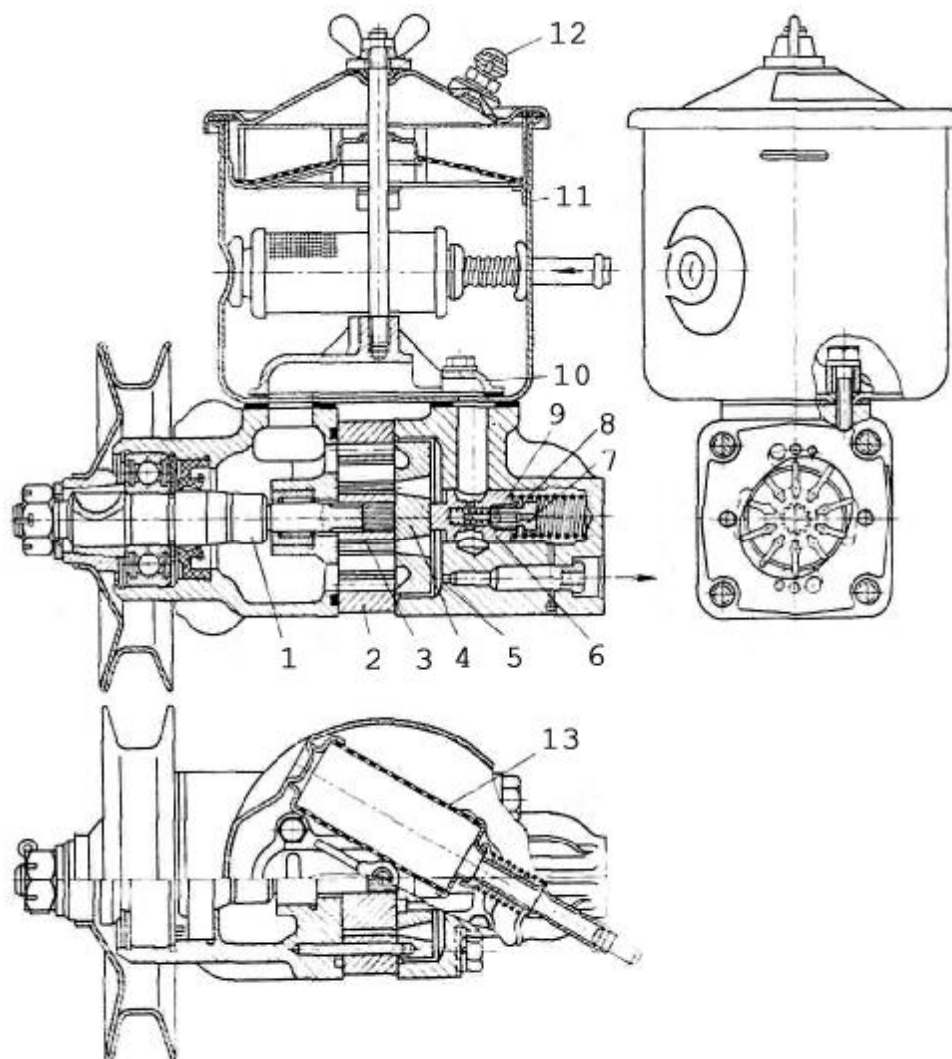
Пластинчатый гидронасос ГУР а/м "ЗИЛ": 1 – приводной вал; 2 – статорное кольцо; 3 – ротор; 4 – распределительный диск; 5 - дросселирующее отверстие; 6 – перепускной клапан; 7 – седло предохранительного клапана; 8 – пружина; 9 – предохранительный клапан; 10 – коллектор; 11 – бачок; 12 – сапун; 13 – сетчатый фильтр.
